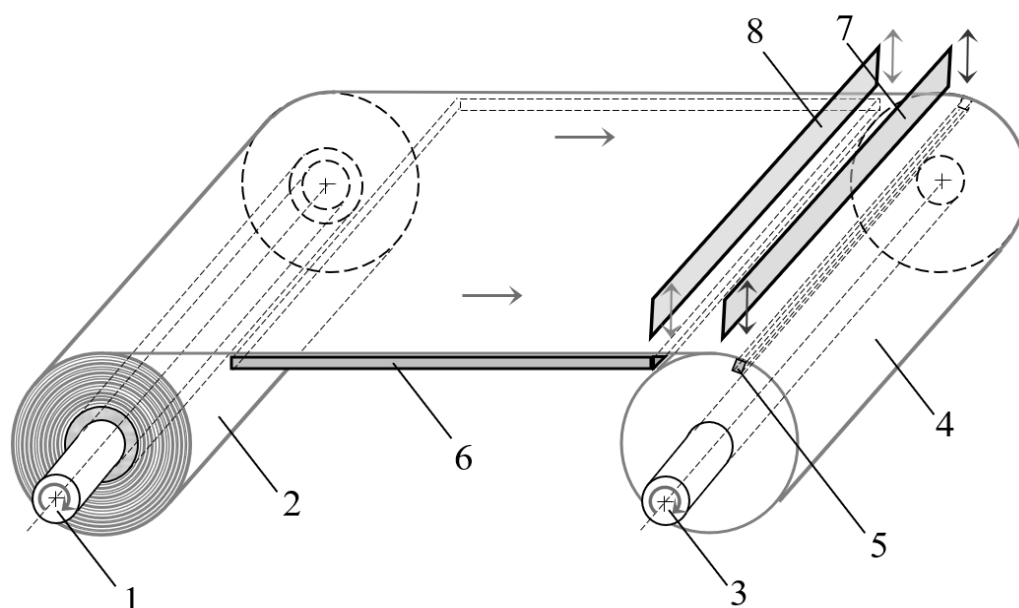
Загальний вигляд пристрою для виготовлення ковбасних оболонок циліндричної форми із багатофункціональної плівки
